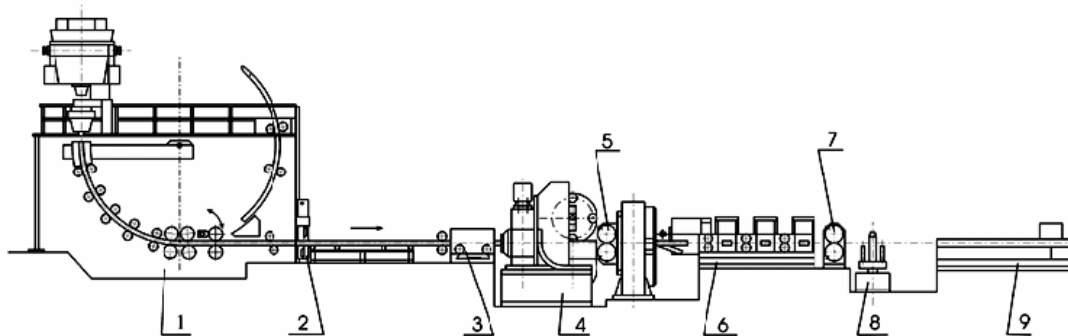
Схема ливарно-прокатного агрегату з планетарним станом для дрібного сорту і катанки:
